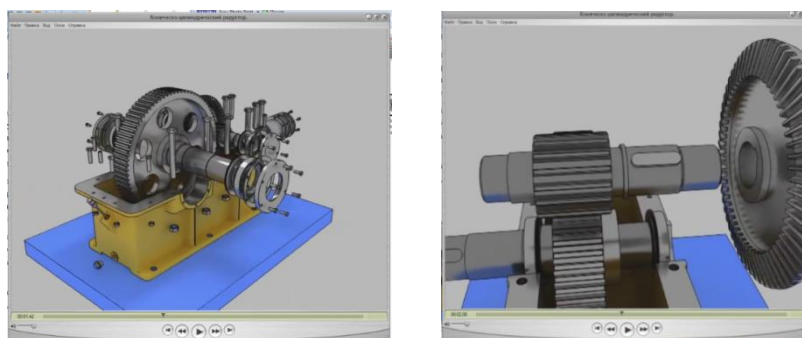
Кадры из фильма «Соединение деталей редуктора»
